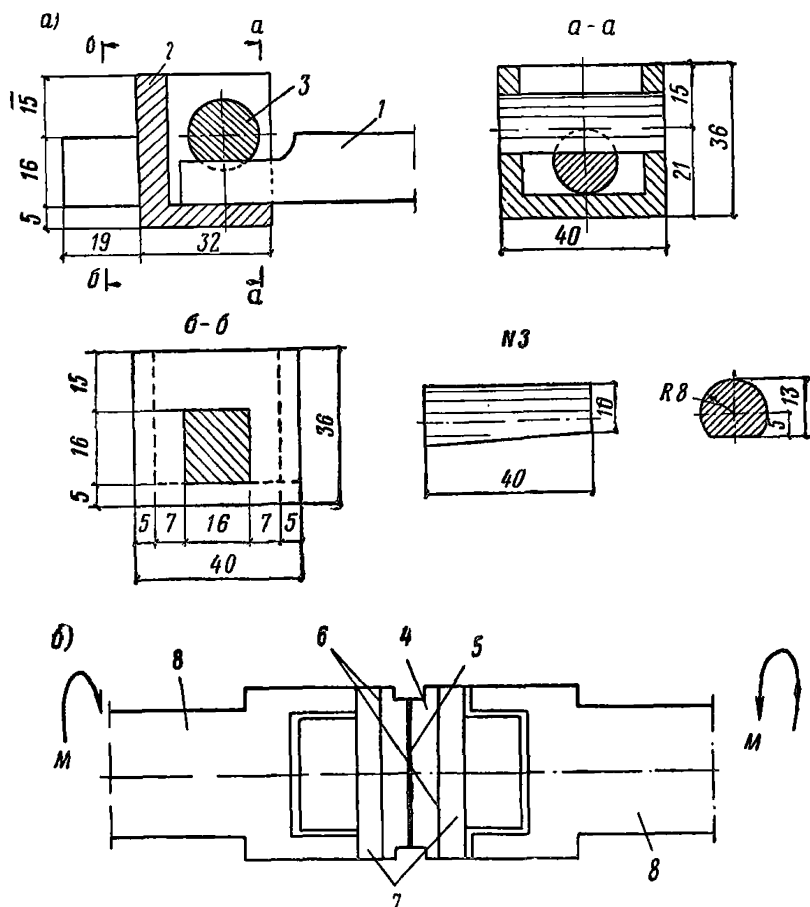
Приспособление для испытания образцов на сдвиг при кручении
